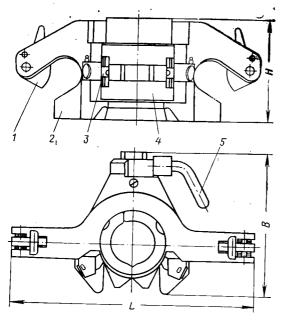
Элеватор ЭТАД: 1- предохранитель; 2- корпус; 3- упор; 4- захват; 5- рукоятка
